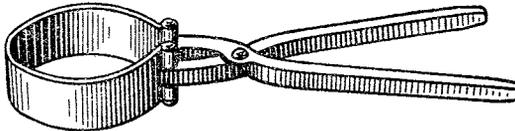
Приспособление для установки поршня с кольцами в цилиндр двигателя
